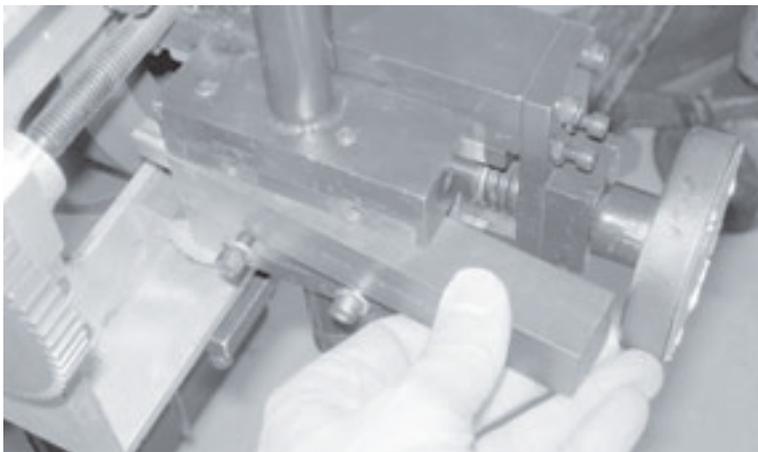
Lösen Sie die Schrauben auf der Werkzeughalterplatte, damit der Werkzeughalter in den Werkzeugschlitten eingepasst werden kann.
